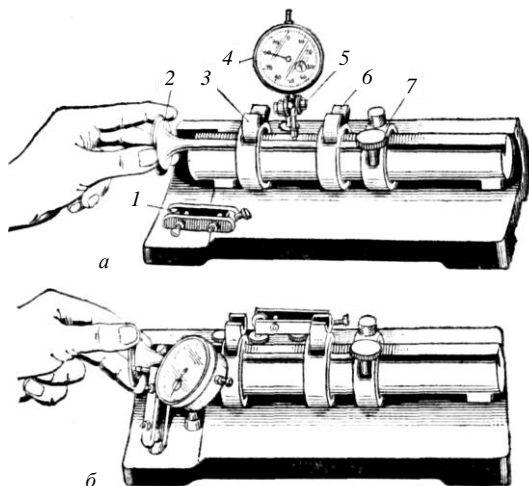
Проверка клапана на индикаторном приспособлении: *а* – проверка прямолинейности стержня; *б* – проверка биения фаски тарелки; 1, 5 – стойки для индикатора; 2 – клапан; 3, 6 – прижимы; 4 – индикатор; 7 – упор
